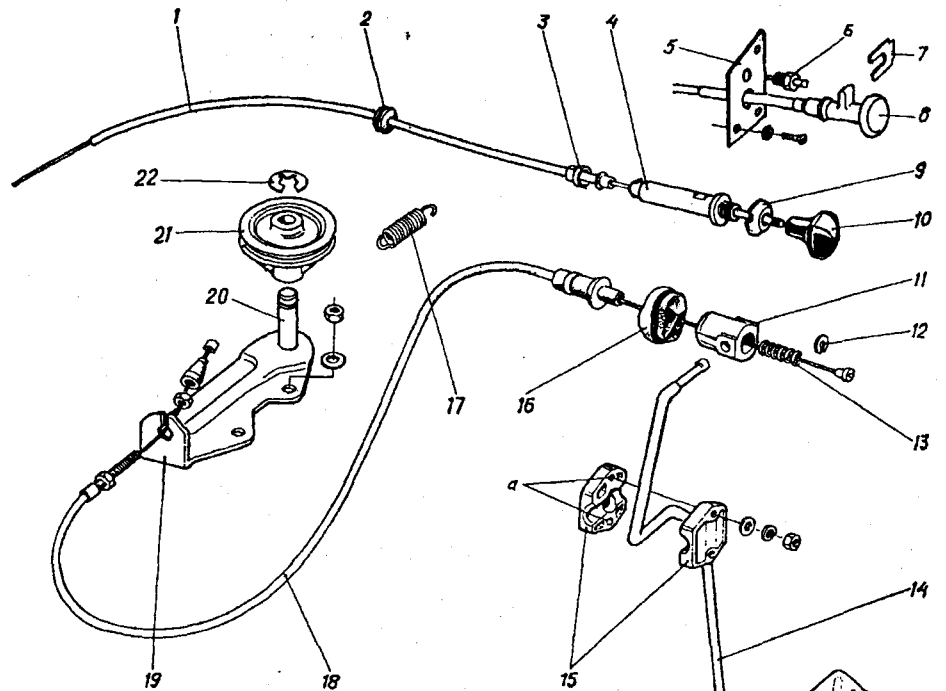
Детали привода карбюратора и их крепление: 1 – оболочка тяги воздушной заслонки; 2 – втулка уплотнительная; 3 – фиксатор; 4 – кронштейн; 5 – кронштейн выключателя; 6 – выключатель; 7 – скоба; 8 – ручка; 9 – гайка; 10 – ручка; 11 – корпус компенсатора; 12 – фиксатор тяги; 13 – пружина компенсационная; 14 – педаль акселератора; 15 – опора; 16 – упор; 17 – пружина; 18 – тяга дроссельной заслонки в сборе; 19 – кронштейн; 20 – ось; 21 – шкив; 22 – кольцо стопорное
